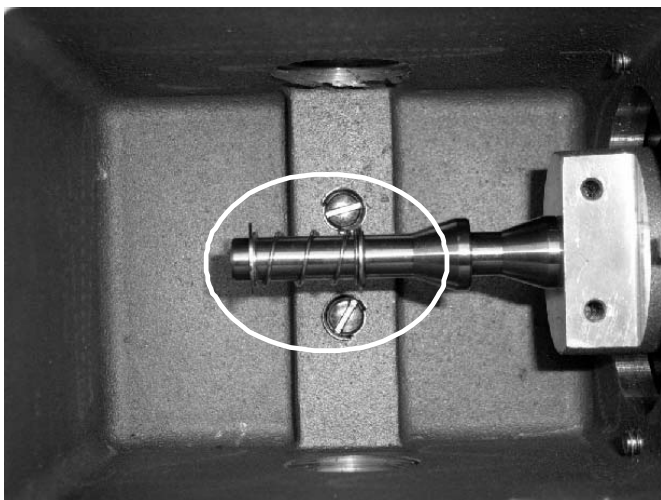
Conjunto de interruptor, suporte de mola, mola com arruelas e parafusos de máquina com arruelas.
